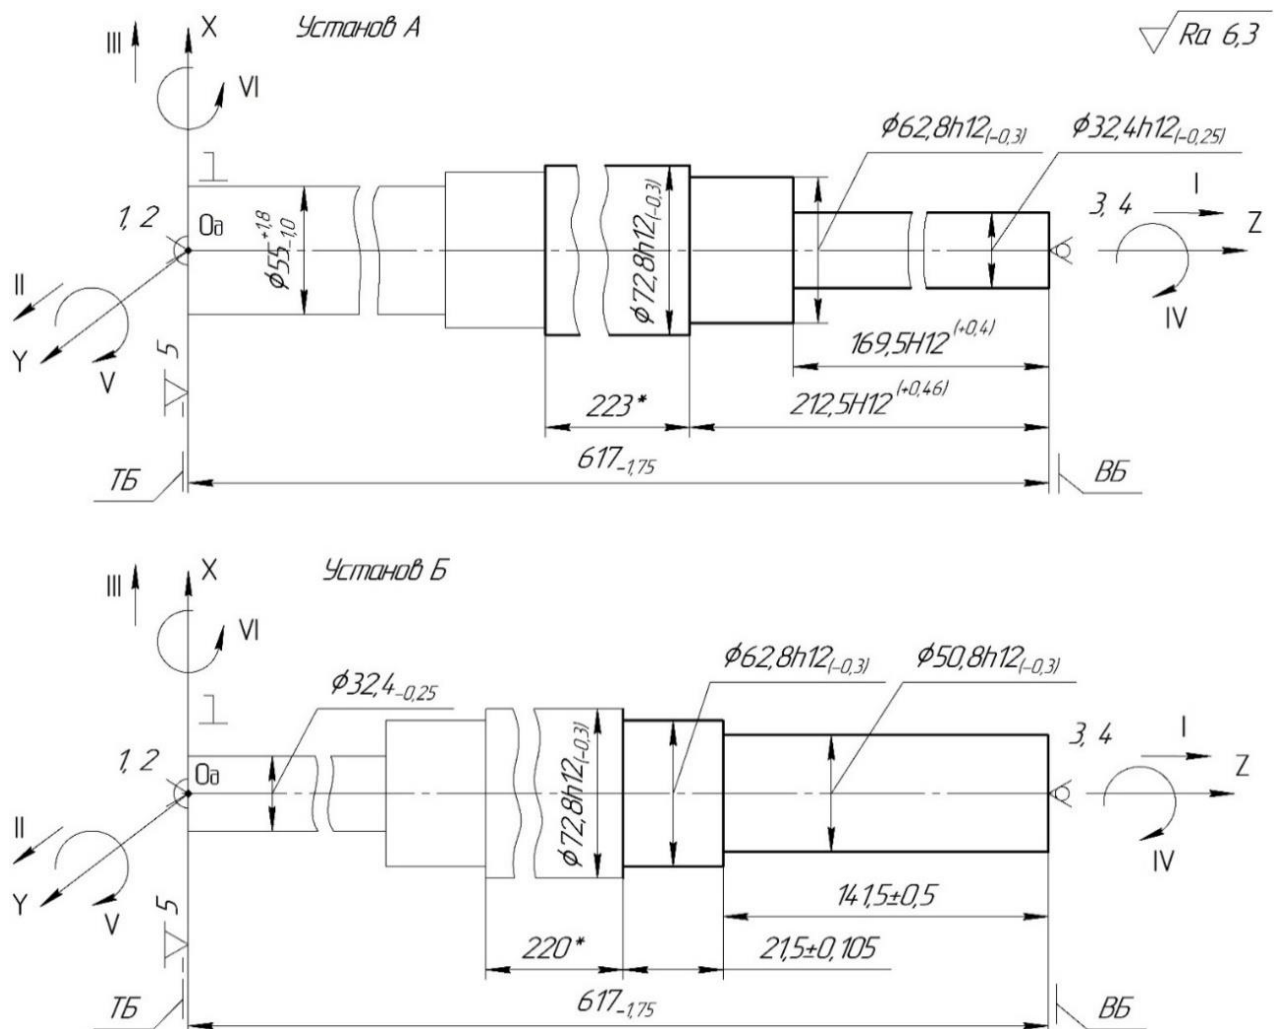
Ескізи заготовки на операції 020 (Установи А і Б). Схема №1
